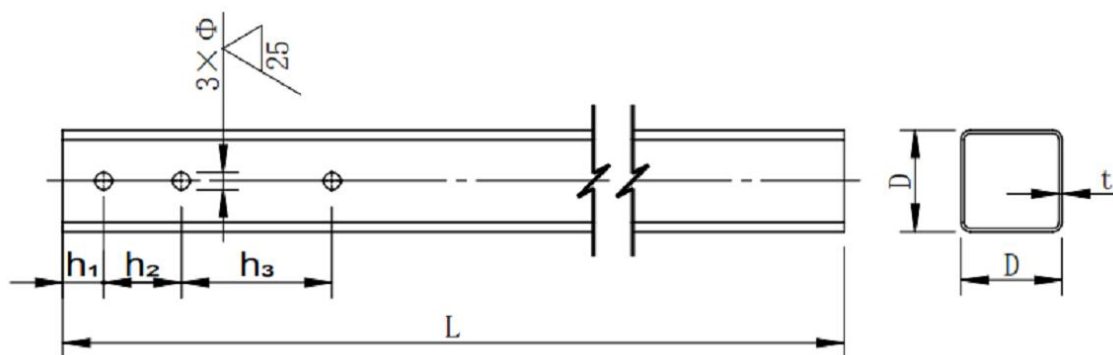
QLZ0-SA (SS) 方管立柱(尺寸单位: mm)
